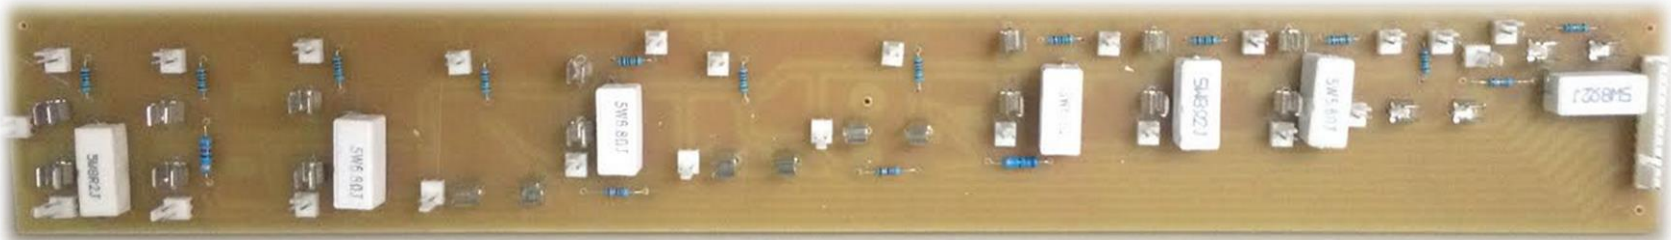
Dispositivos instalados en la tarjeta PCB.
